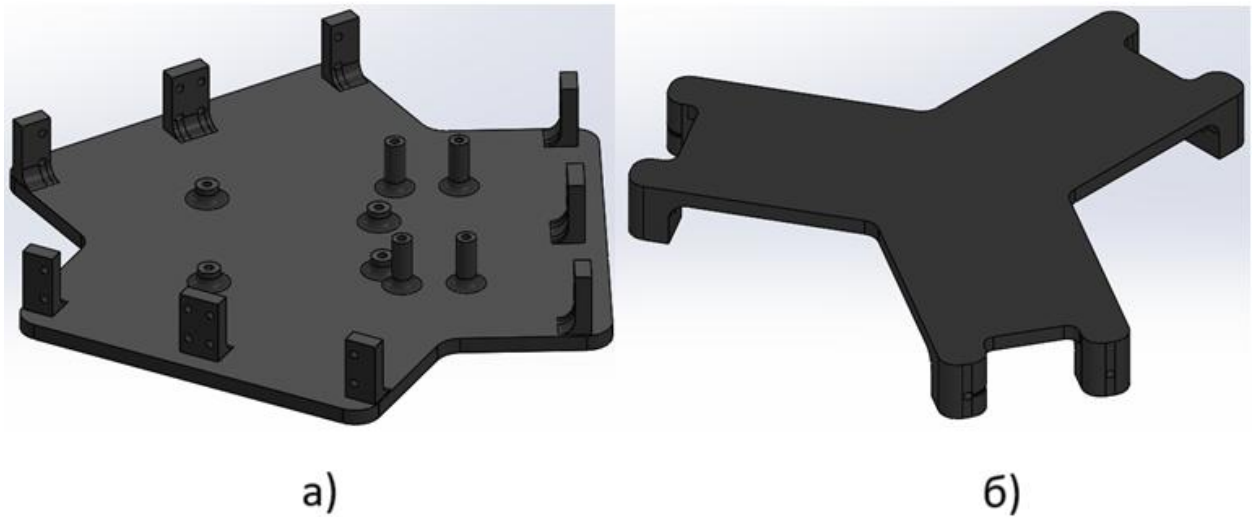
Основні несучі елементи макета: а) нижня база з посадковими місцями; б) верхня рухома платформа
